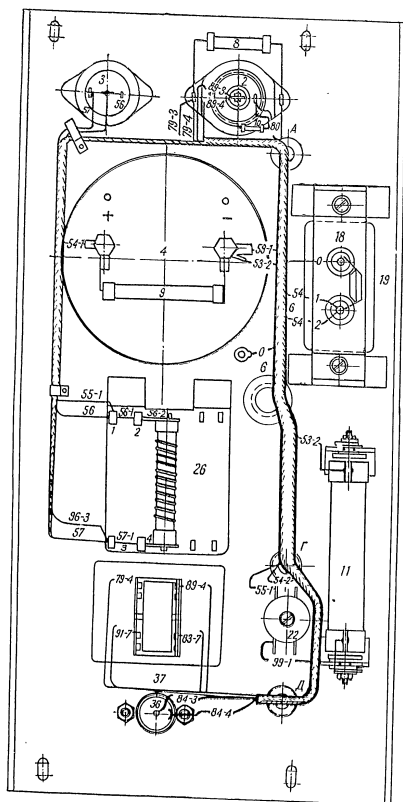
Монтажная схема штифта ШБ-01 блока ША-02
